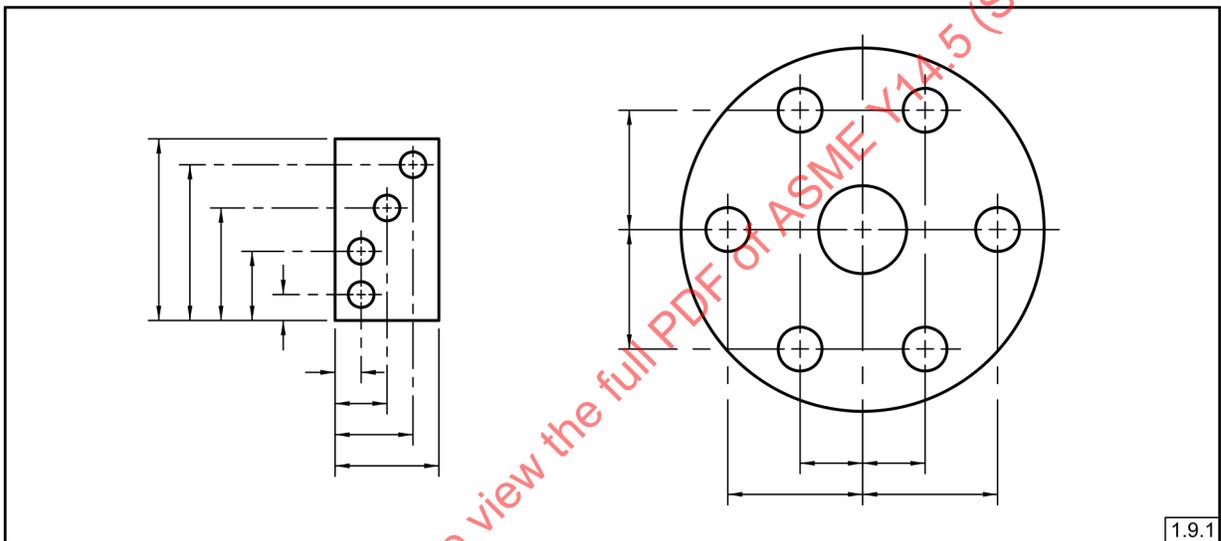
Dimensionado con Coordenadas Rectangulares
